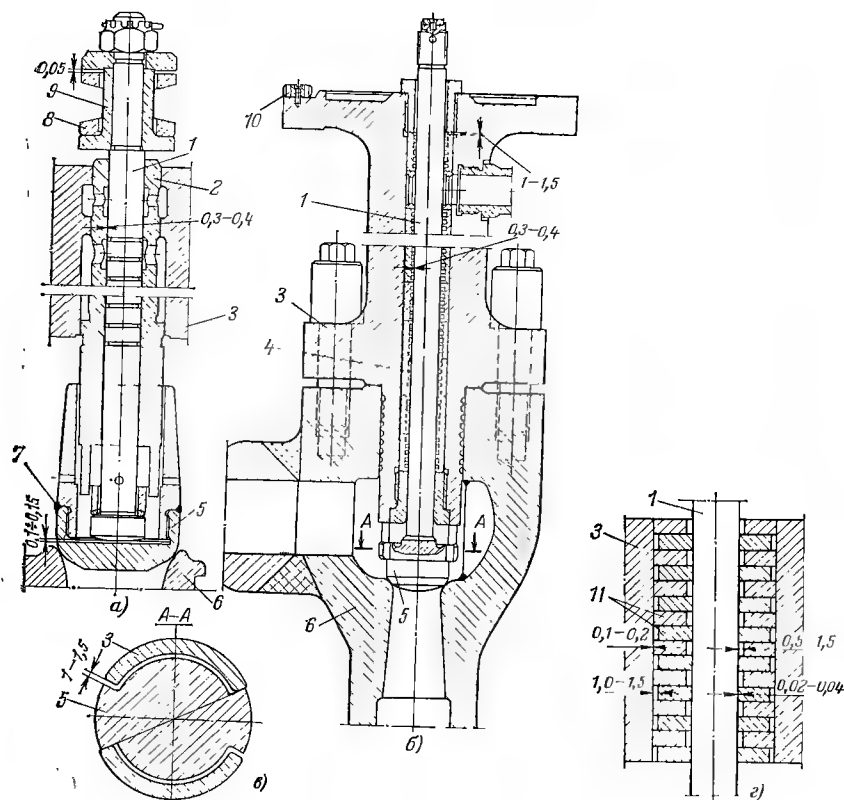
Допуски на зазоры в уплотнениях штоков регулирующих клапанов высокого давления.
